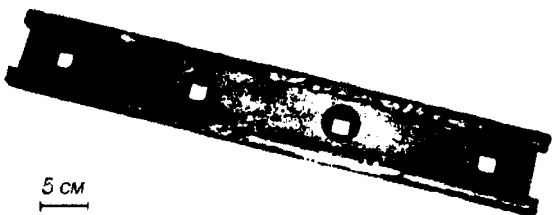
Внешний вид ножа кормоуборочного комбайна с износостойким покрытием на режущих кромках.
